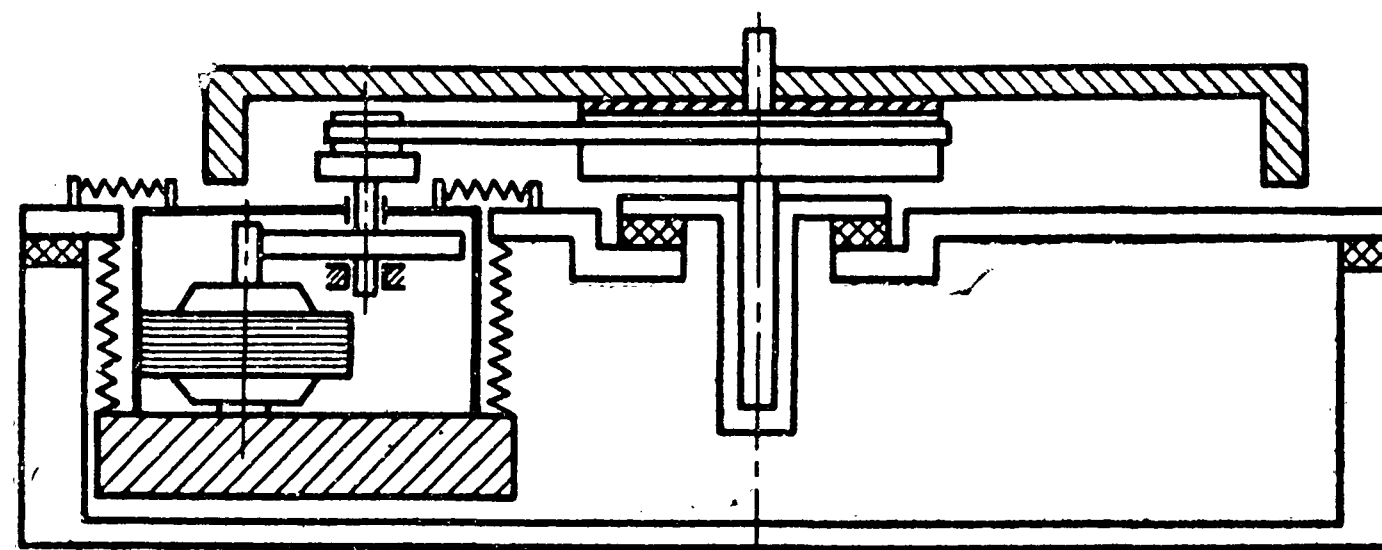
Схема движущего механизма с использованием высокооборотного электродвигателя.
